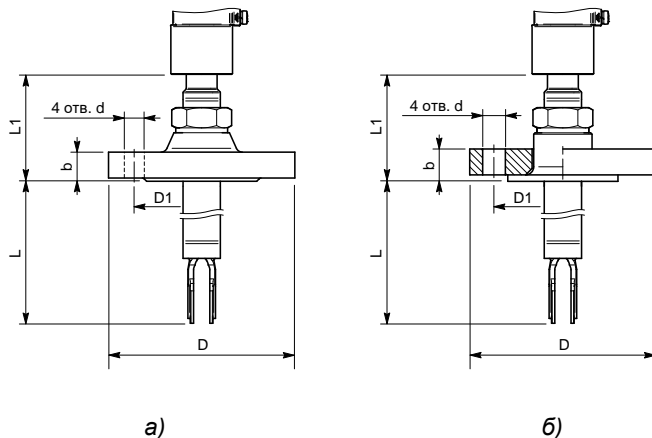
Размеры сенсорной части с фланцевым присоединением (код Fxx):
